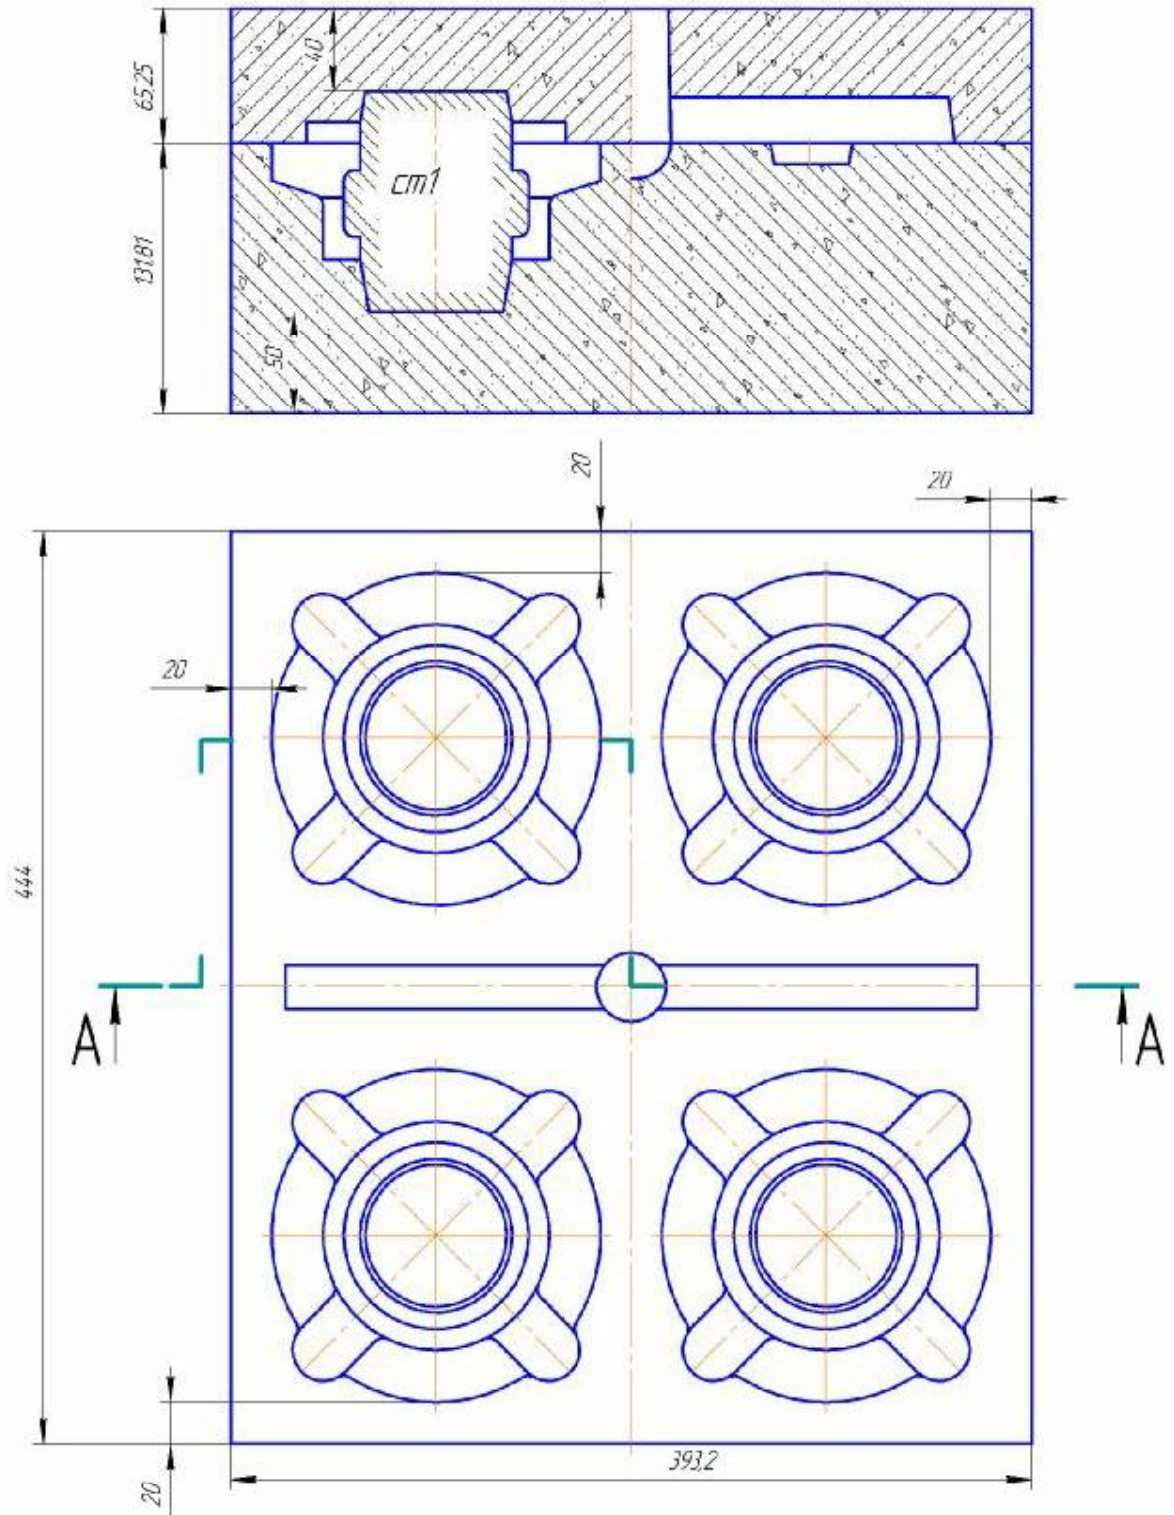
Форма для четырех отливок с минимальными размерами
